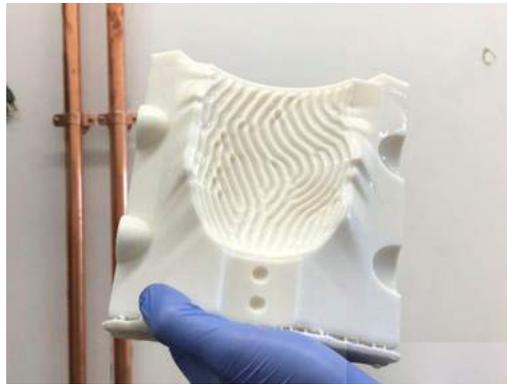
Sección de molde impresa en 3D (Nervous System, INC, 2018)
